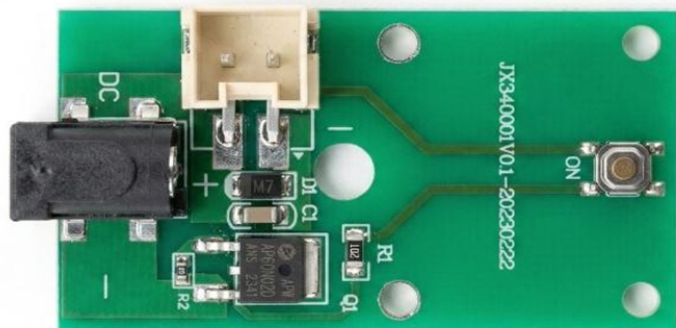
Placa de circuito impreso (PCB) por JLCPCB
